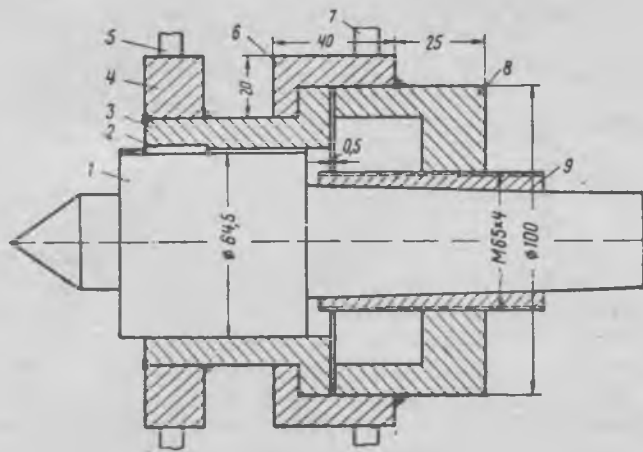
Подвижной центр для вращения тягового двигателя без разборки карданного шарнира:
